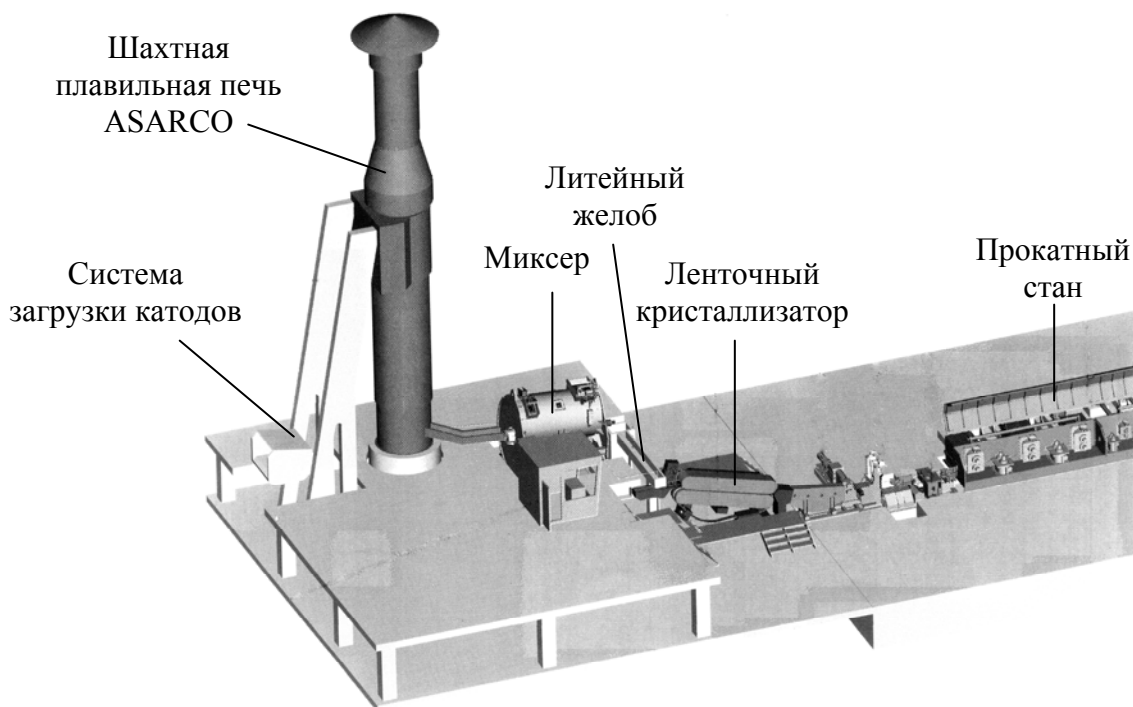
Схема установки литья медных заготовок в ленточный кристаллизатор
